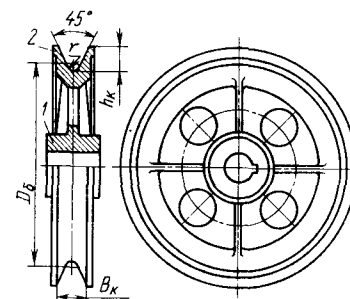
Канатный блок: 1 — ступица; 2 — обод
